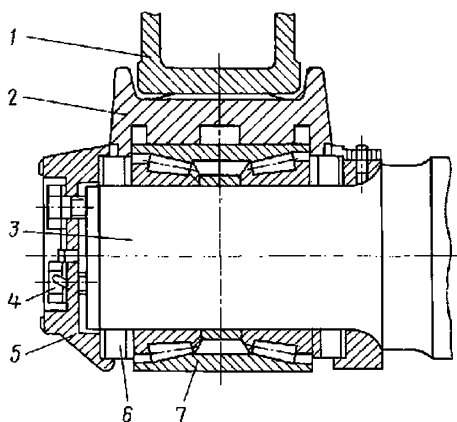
Бескорпусный буксовый узел с кассетным роликовым подшипником вагонов
